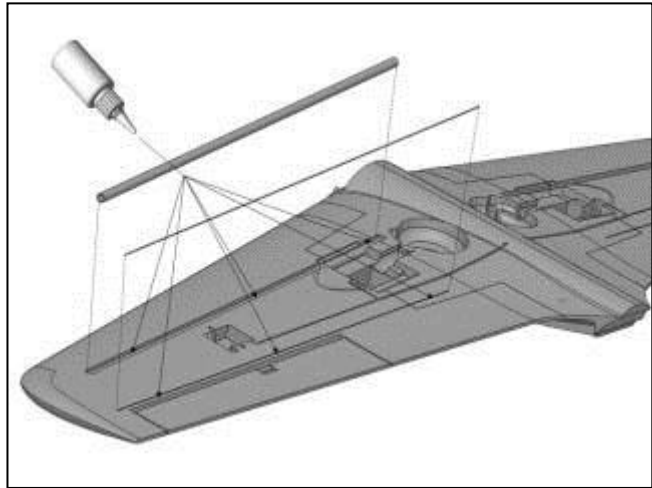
Zuerst die Tragfläche rechts von oben auf das Mittelstück aufsetzen und ausrichten. Zuvor auf die Verbindungsflächen Kleber aufbringen.
